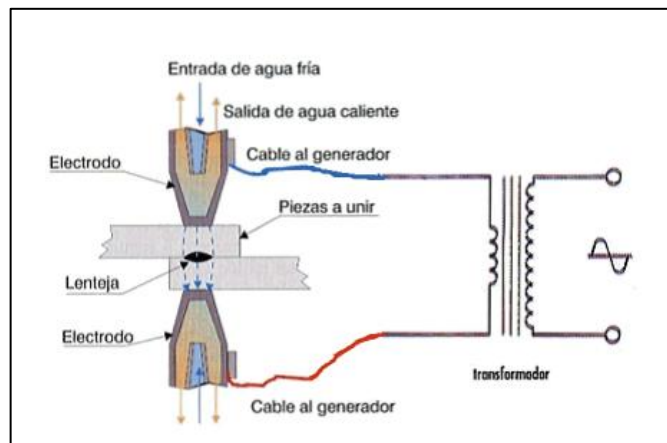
4: Diagrama esquemático del proceso de soldadura RSW
